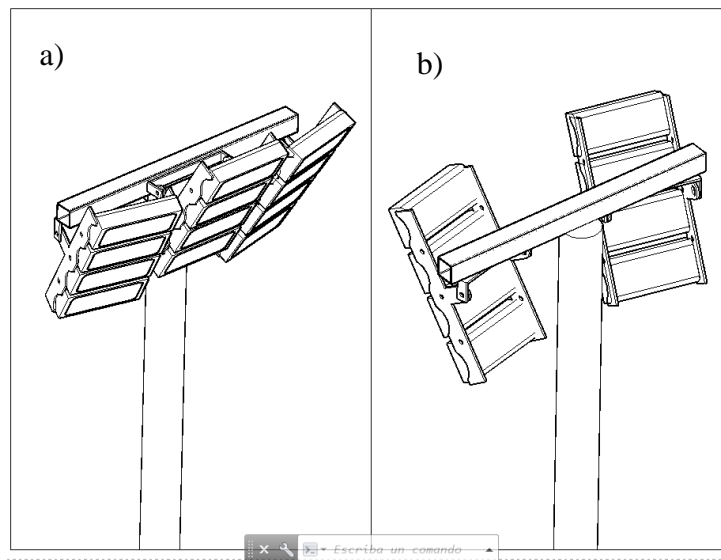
Montaje en parte superior de mástil. a) Cancha de Ecuavoley y b) canchas de Básquet. AutoCAD
